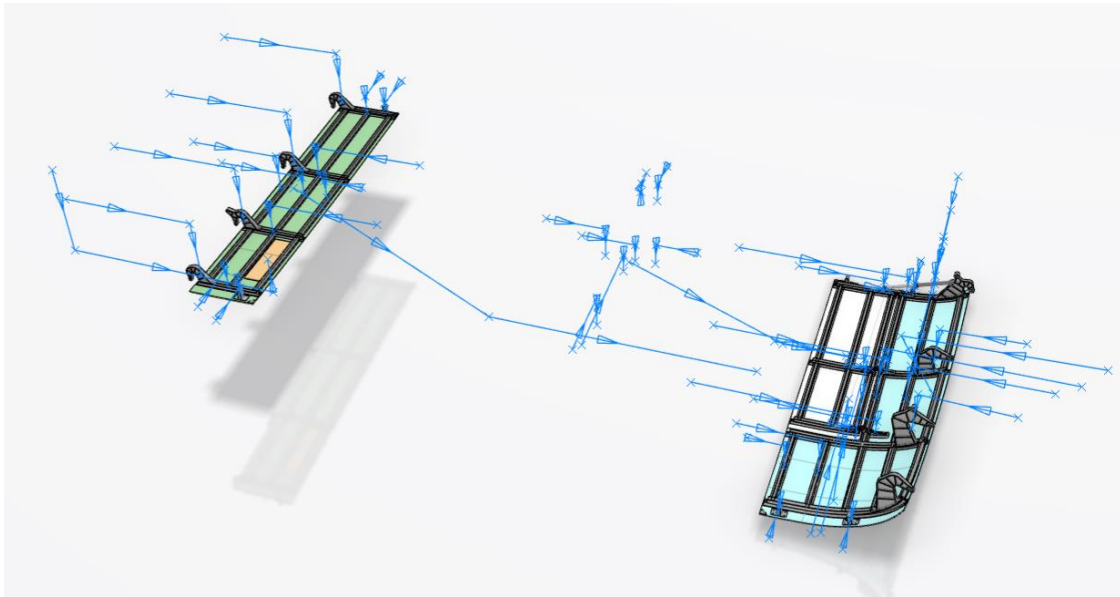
Ensamblaje: Puertas exterior y auxiliar ensambladas. Posicionado de las mismas y montaje de las bisagras antes omitidas. Montaje del cilindro actuador
